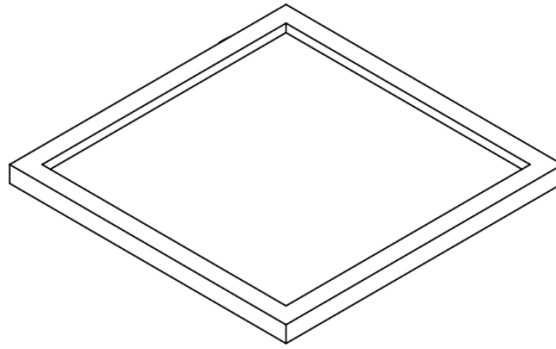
Perspectiva isométrica molde - inflamabilidad
